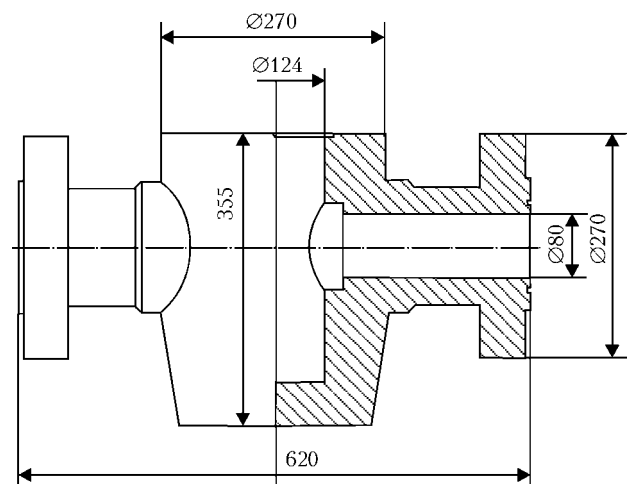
Корпус фланцевой задвижки для работы при давлении 70 МПа
